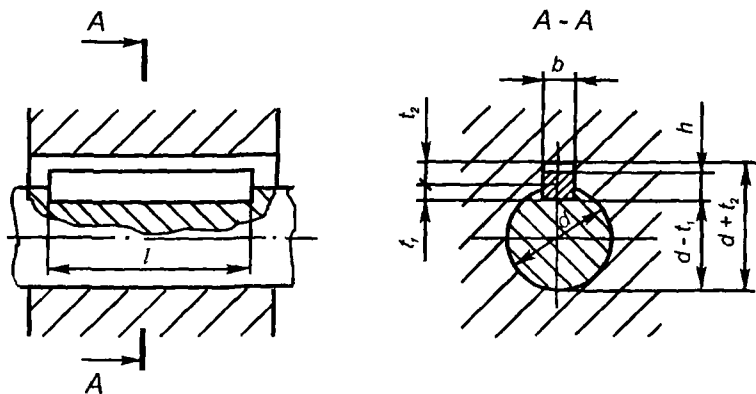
Основные размеры соединения с призматической шпонкой, где  $h$  – высота шпонки;  $t_1$  – глубина паза вала;  $t_2$  – глубина паза втулки;  $b$  – ширина шпонки и пазов втулки;  $d$  – диаметр сопряжения;  $l$  – длина шпонки и паза вала
